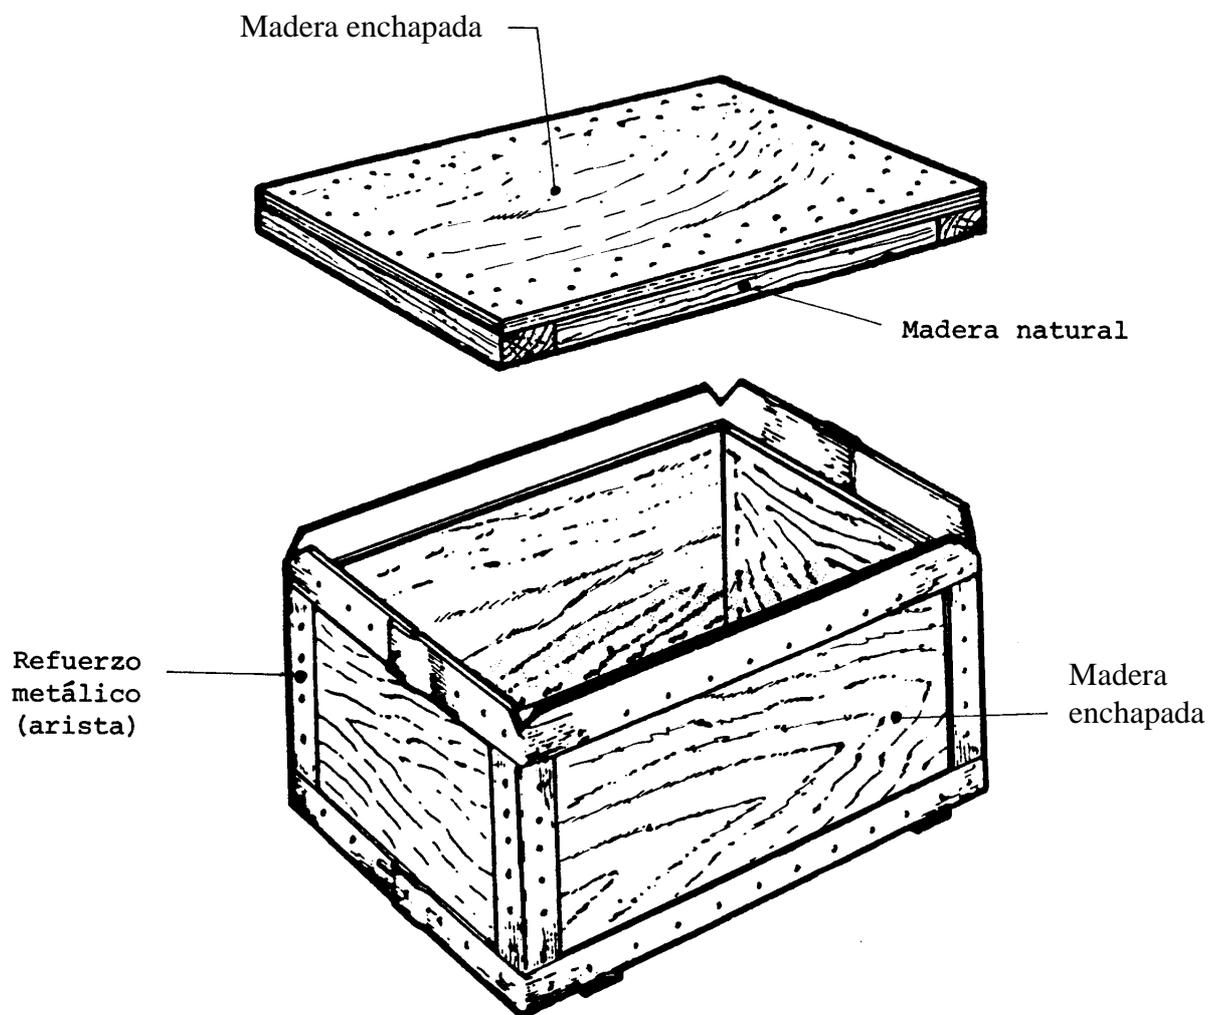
Caja de madera enchapada, construcción con refuerzo metálico de las aristas
